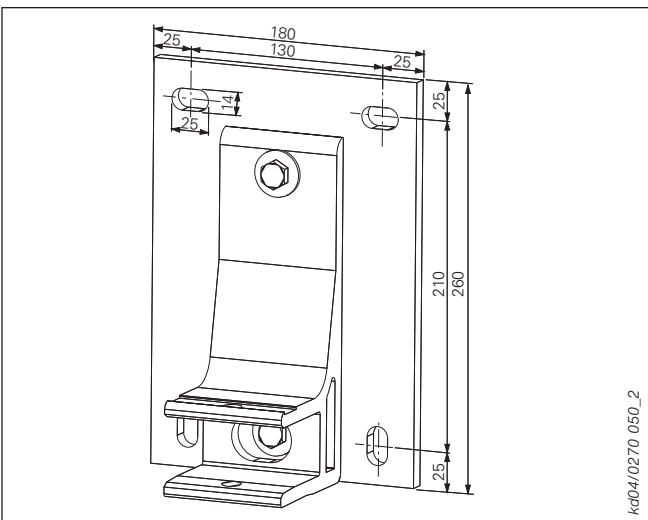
Consola tipo C – Fijación mural con placa de montaje pequeña 630/650/730/740/750
